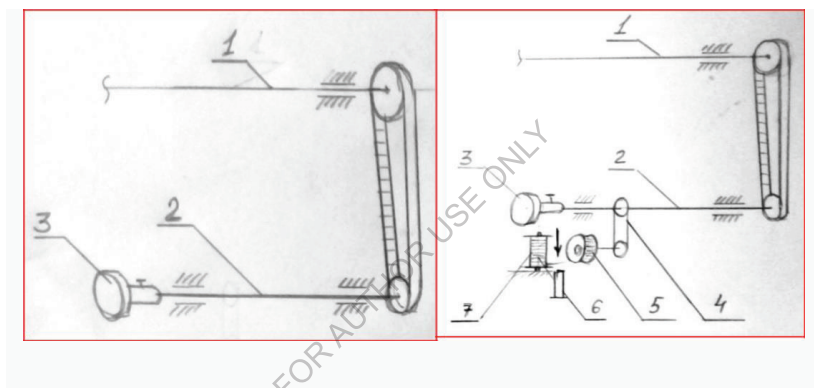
Автоматическая заправка челночного шкива устройства существующей и предлагаемой схемы.
